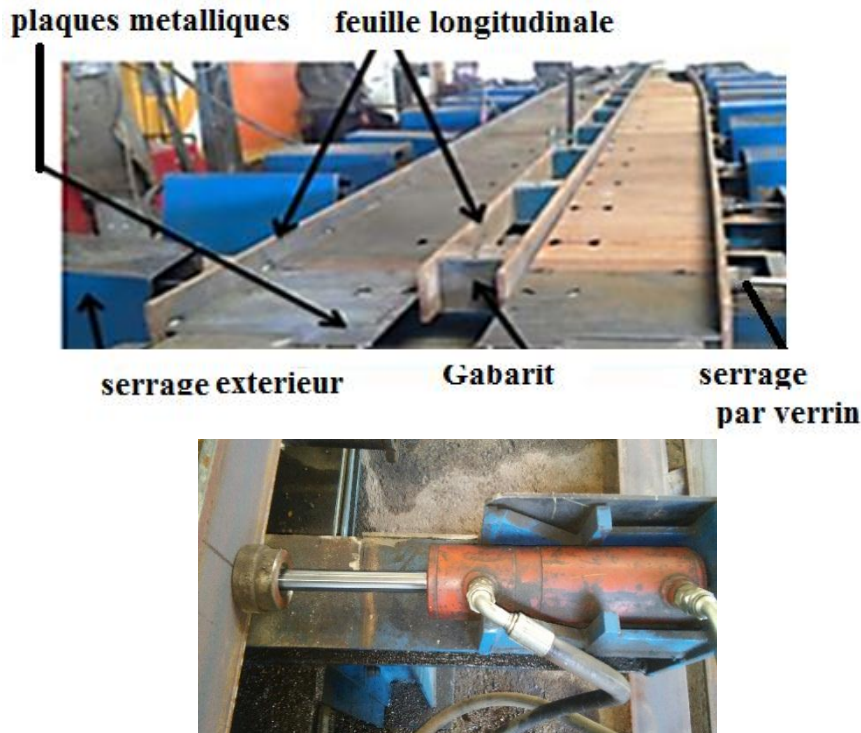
Fixation des tôles pour soudage -ACI-
